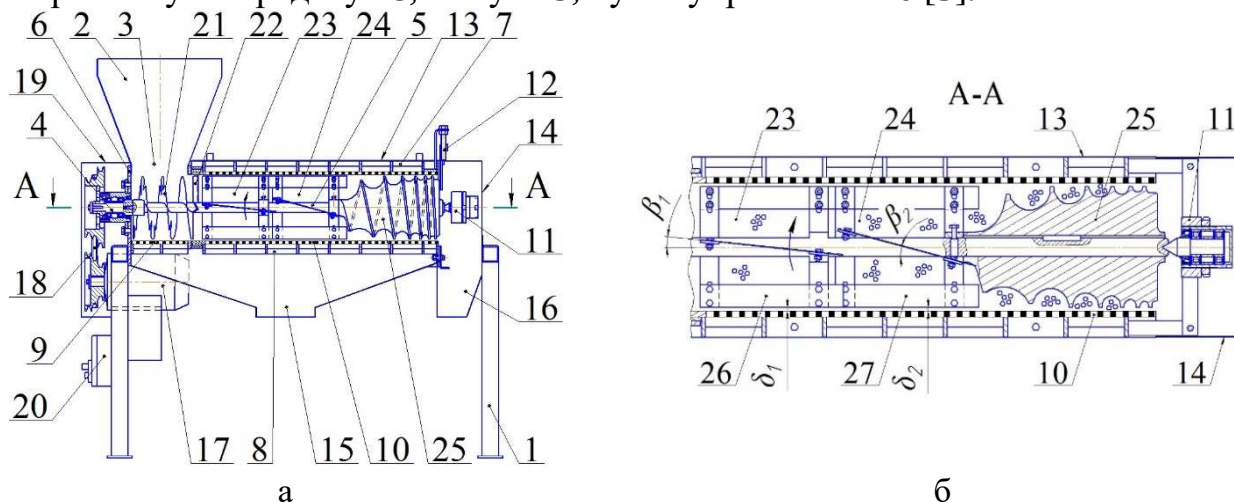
Схематическое изображение выделителя сока из томатов: а – главный вид, б – продольный разрез
